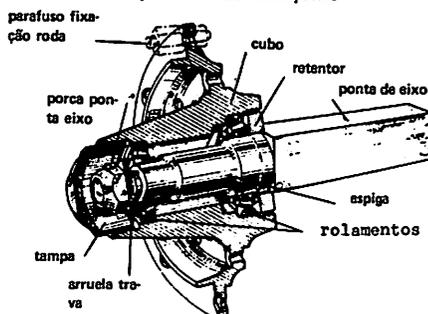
Ponta de eixo, com os elementos de montagem do cubo
